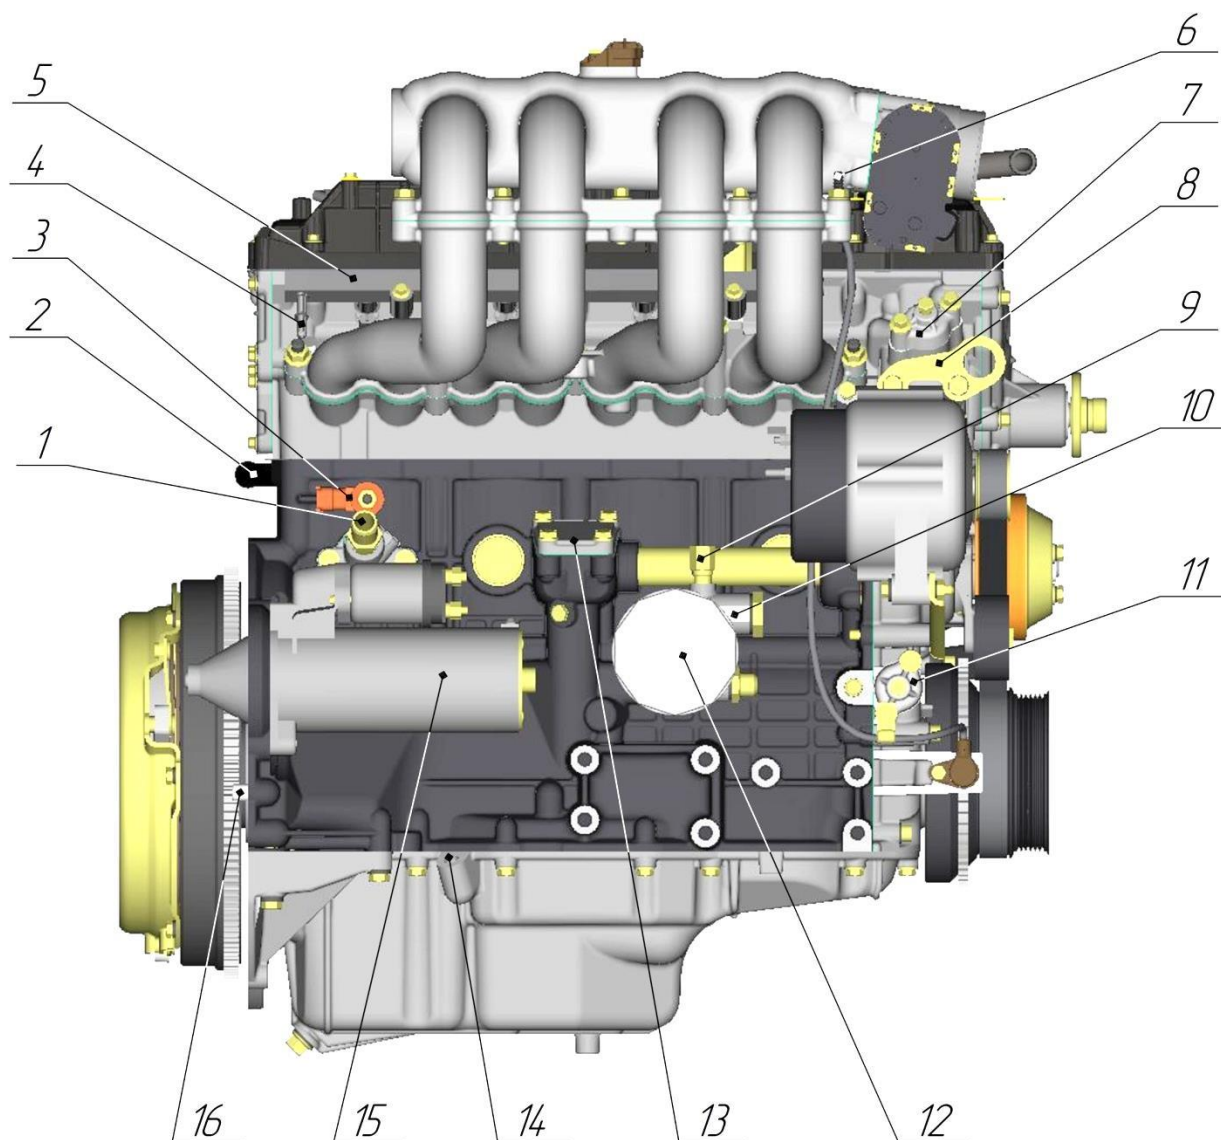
Вид слева двигателя ЗМЗ-40905.10:
